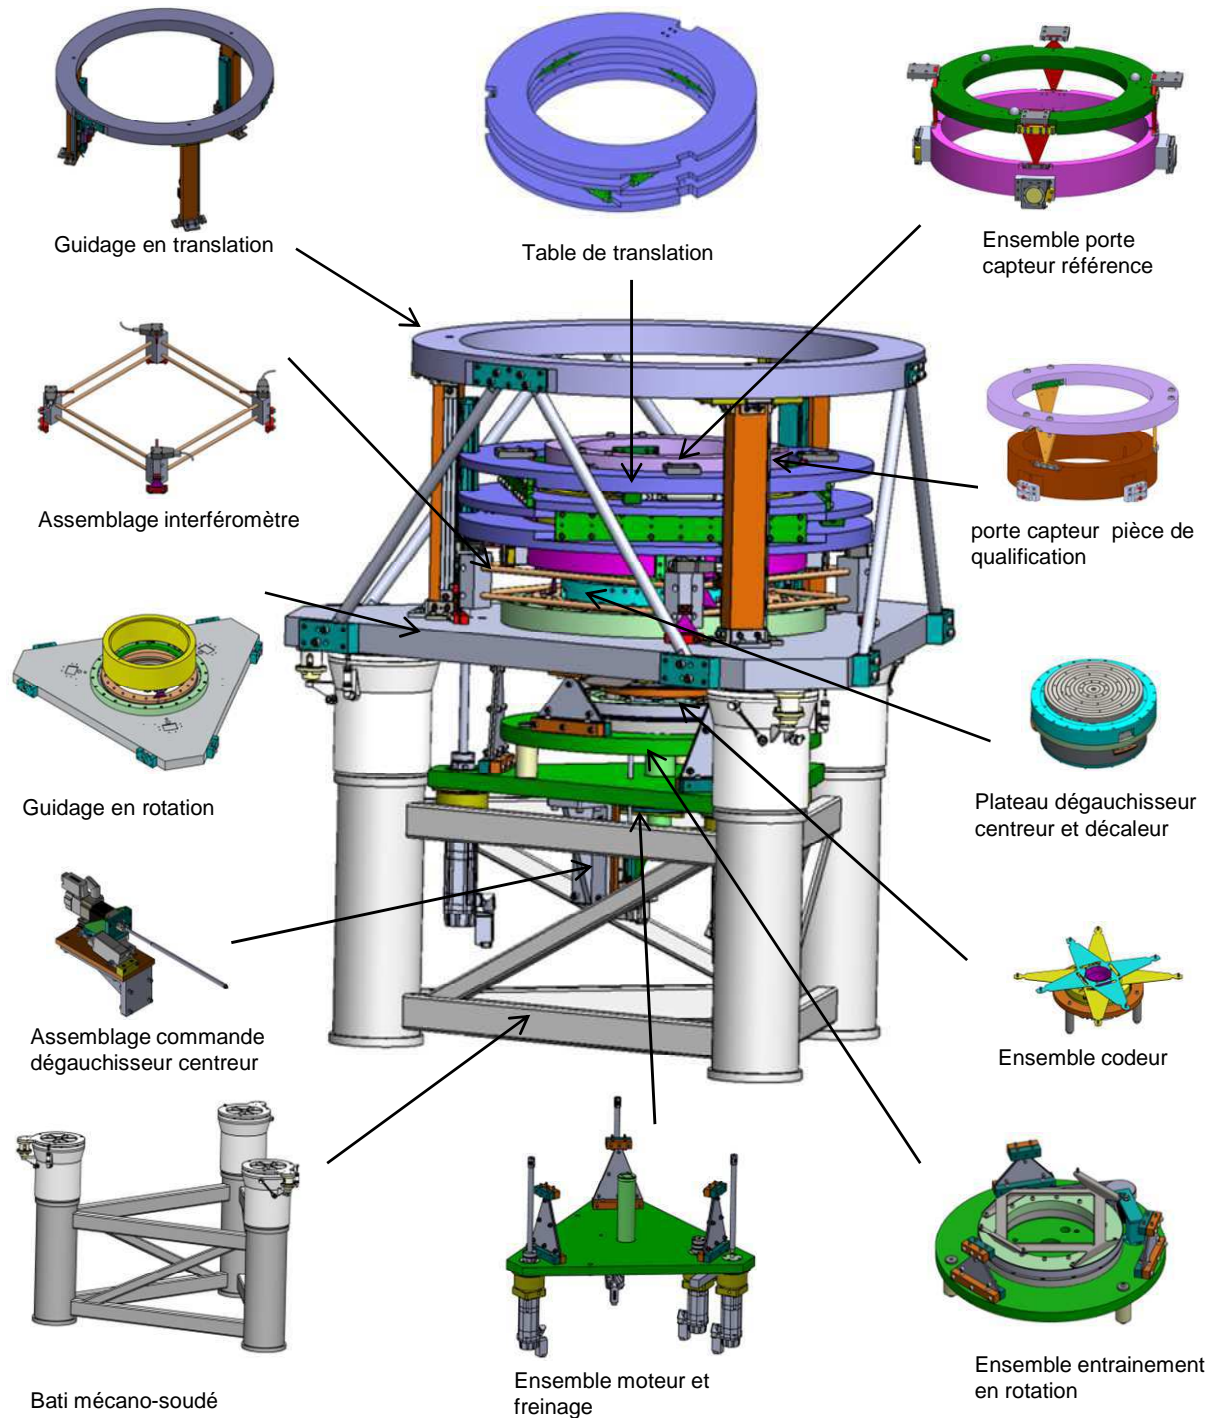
sous ensemble de l'équipement de mesure de cylindricité
